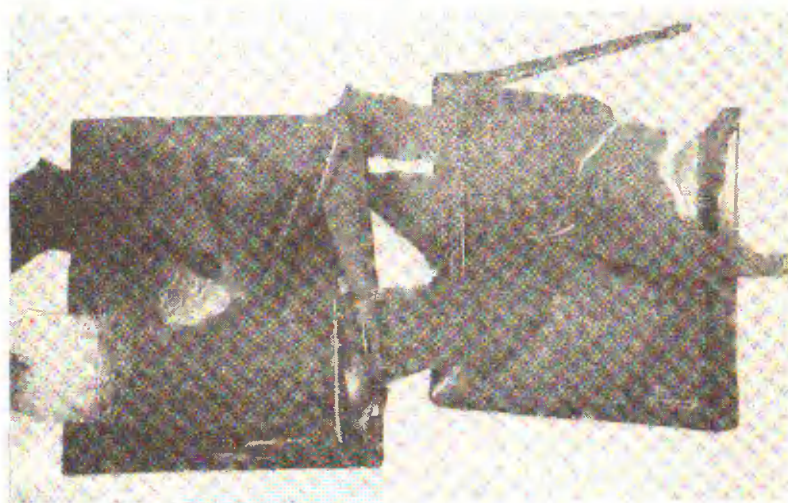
Образцы коробов после испытаний на герметичность опрессовкой внутренних поверхностей сжатым воздухом
